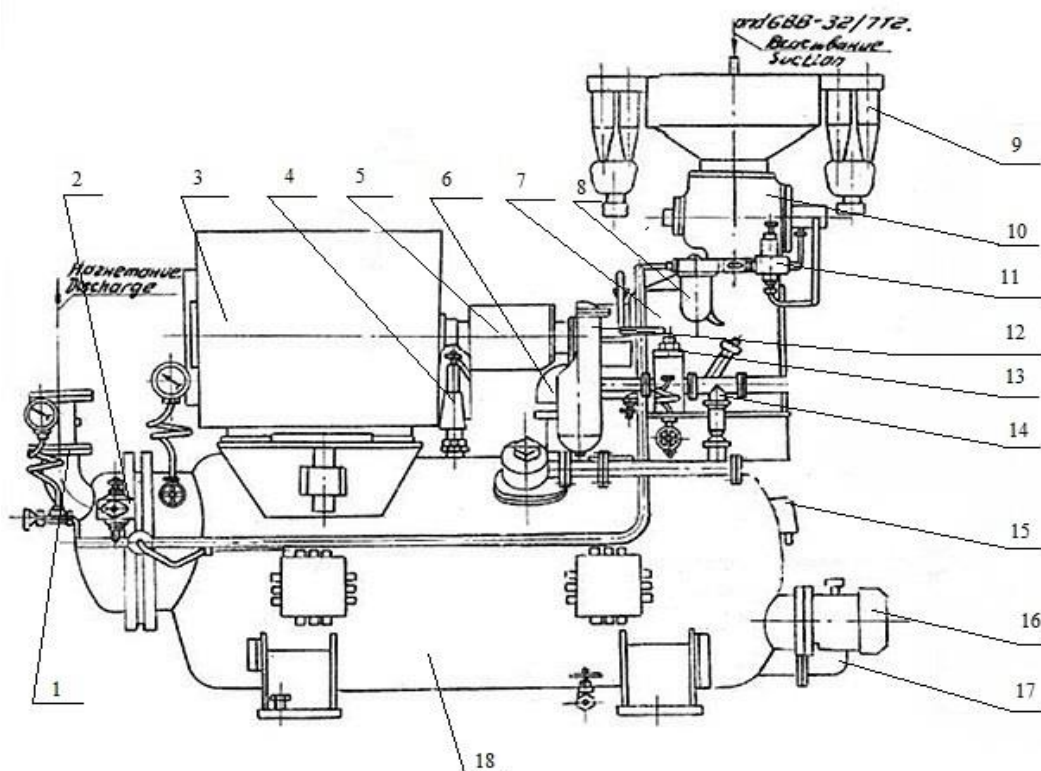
Агрегат компрессорный 6ВВ-32/7
